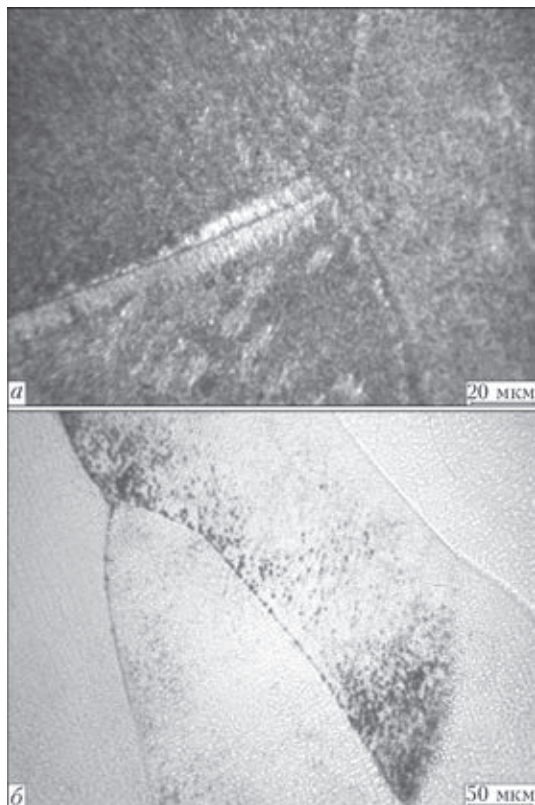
Микроструктура металла сварного соединения титанового сплава Ti-6,5Al-3Mo-2,5V-4Nb-1Cr-1Fe-2,5Zr, выполненного ЭЛС: *a* — ОМ; *б* — металл шва после сварки
